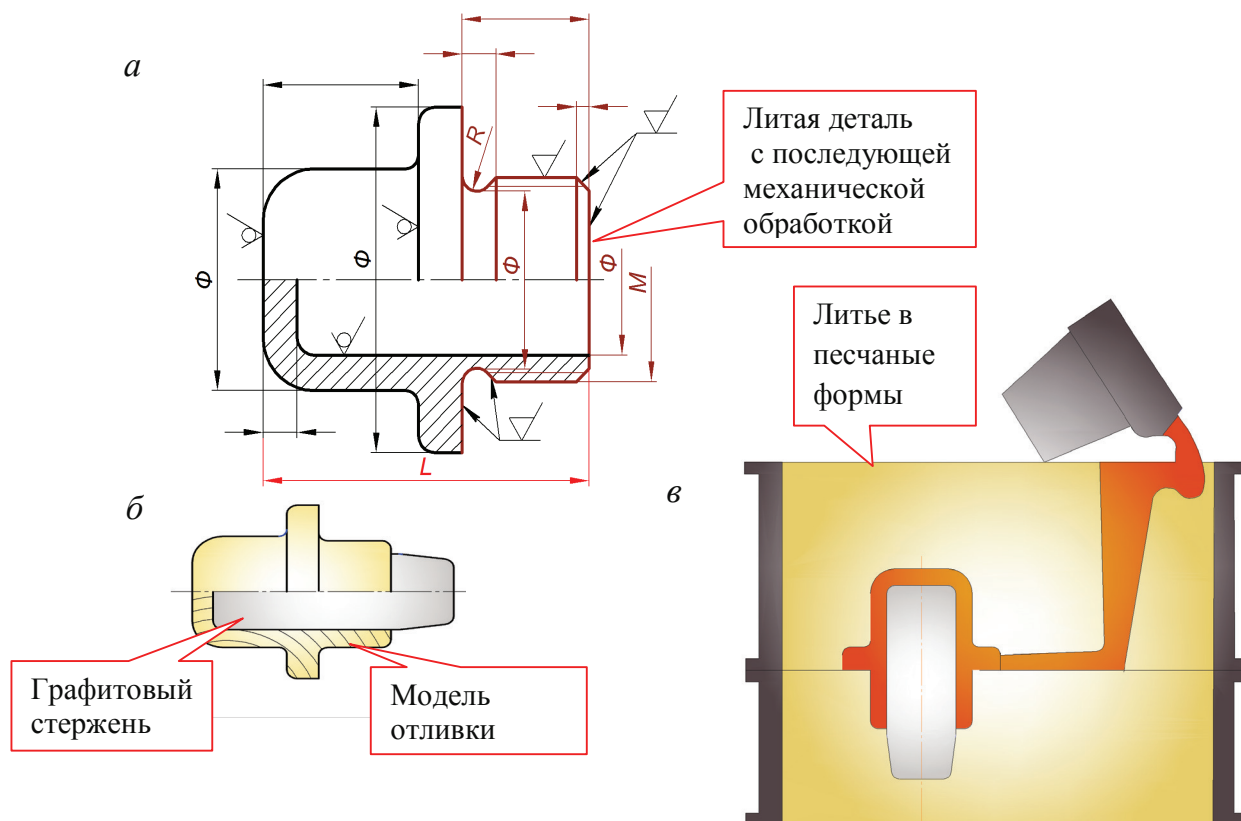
Изготовление детали литьем в песчаные формы с последующей механической обработкой:
